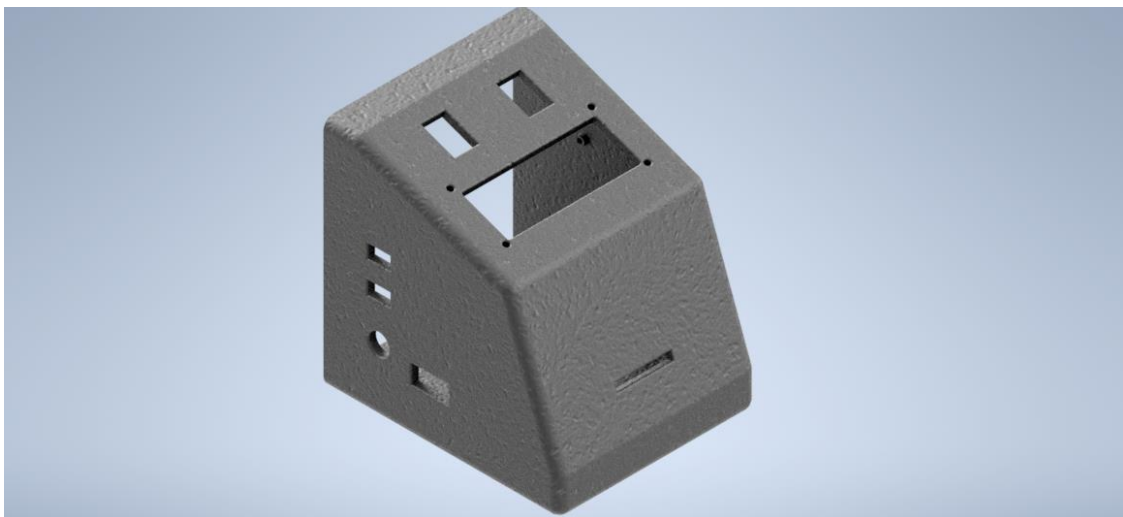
Soporte PCB y componentes electrónicos. (Autores)
